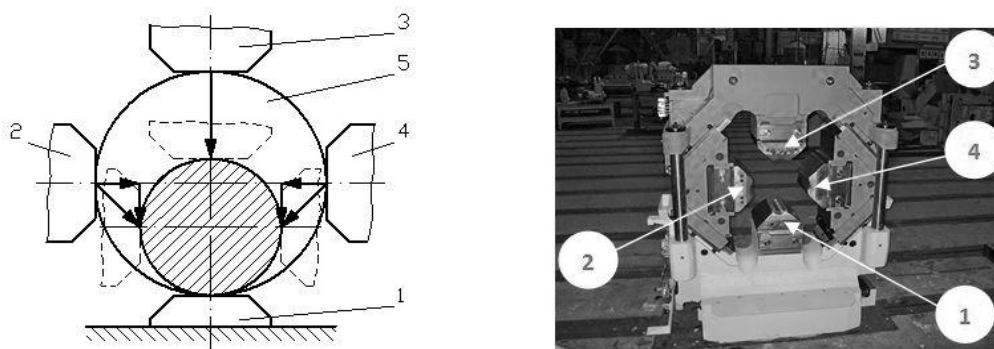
Четырехбойковое ковочное устройство и схема обжатия
